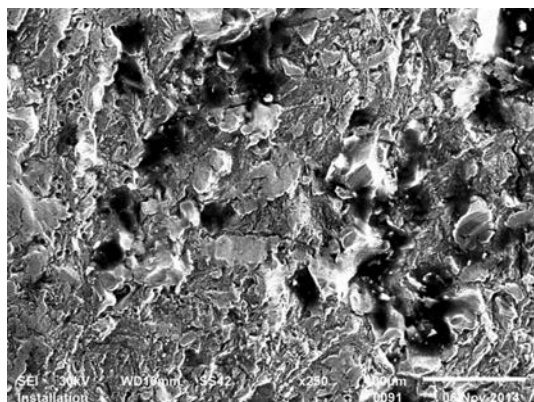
Поверхность трещины у основания зуба в металле шестерни 2
